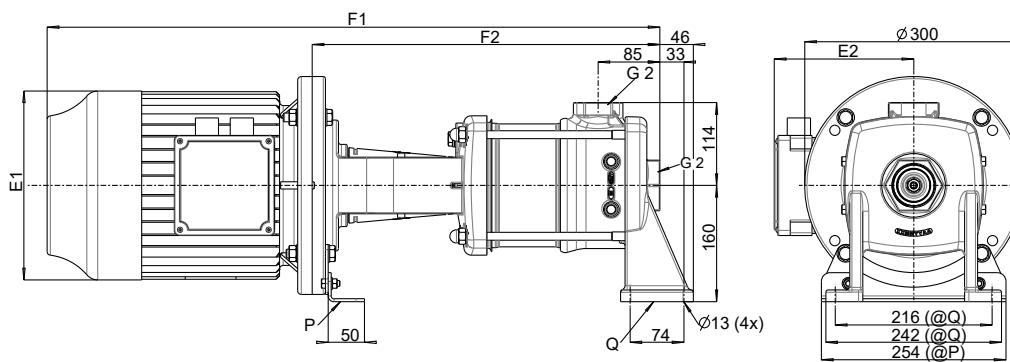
Abmessungen und Anschlüsse DPH(S)I 15 mit Motor V1
